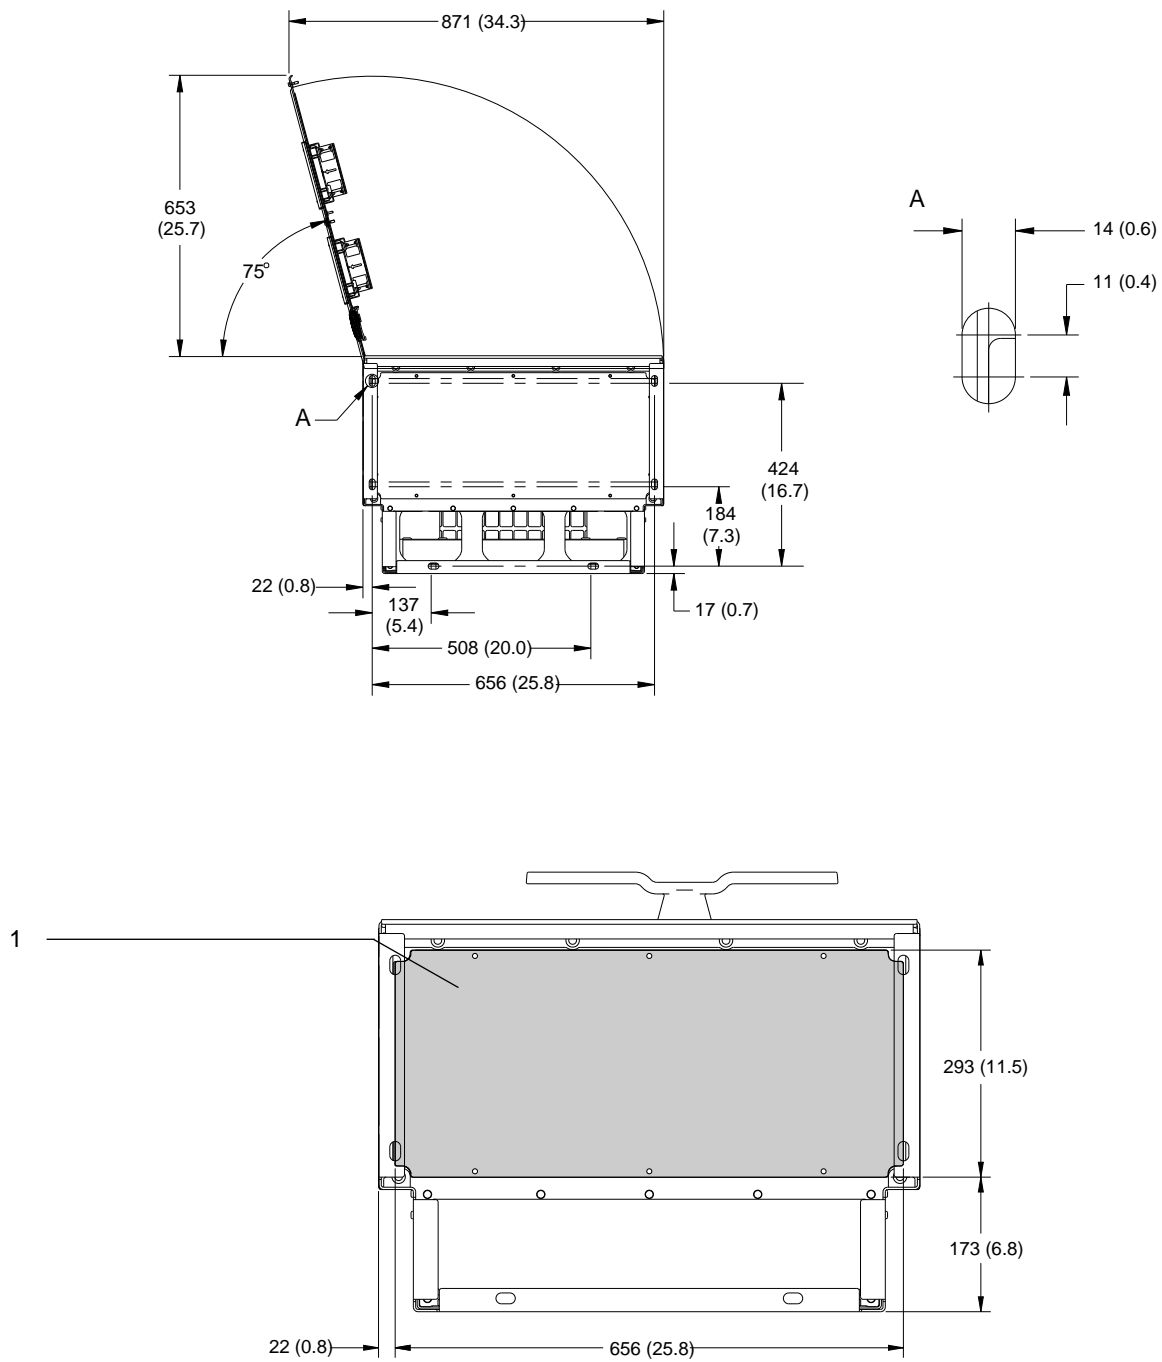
Espace pour la porte et dimensions de la plaque d'entrée des câbles pour E2h
